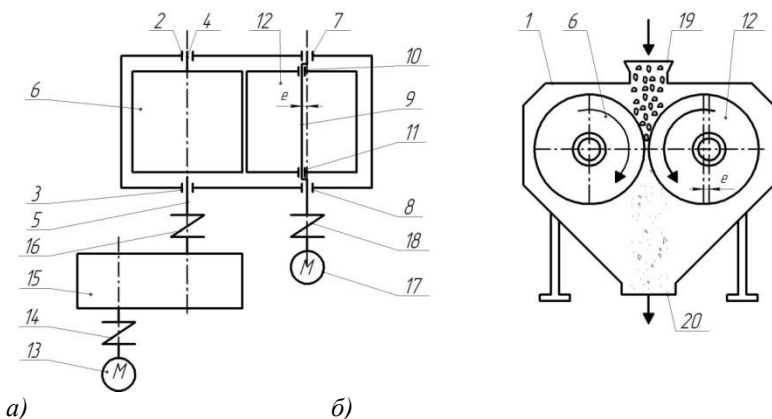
Схема вибровалкового измельчителя: а – вид сверху, б – вид сбоку
